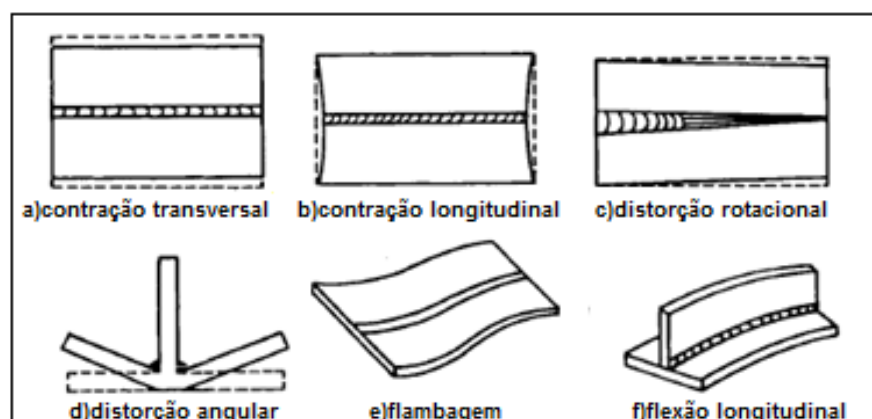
Tipos de distorção na soldagem [Adaptado de Masubuchi, 1980].
